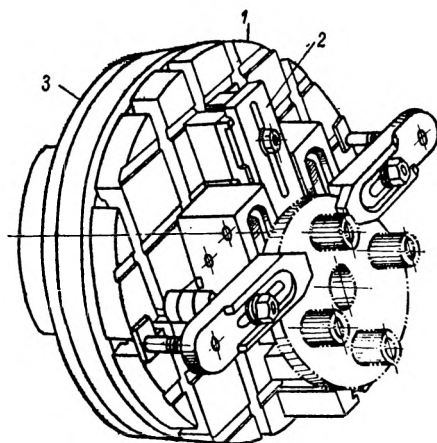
Сборное приспособление с фиксирующими пальцами и планкой.
